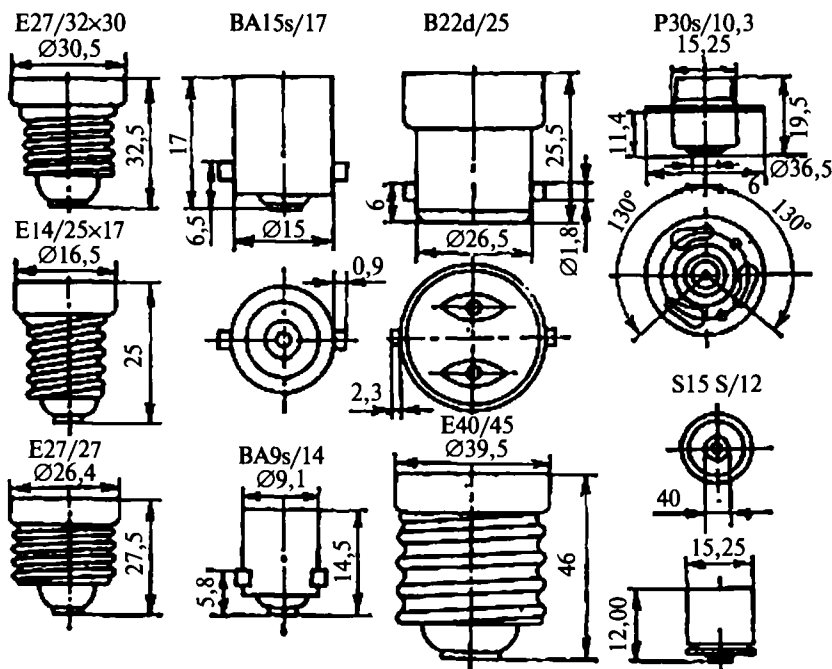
Основные типы цоколей для ЛН: Е — резьбовой; В — штифтовый; ВА — штифтовый для автомобилей; Р — фокусирующий; S — цилиндрический
